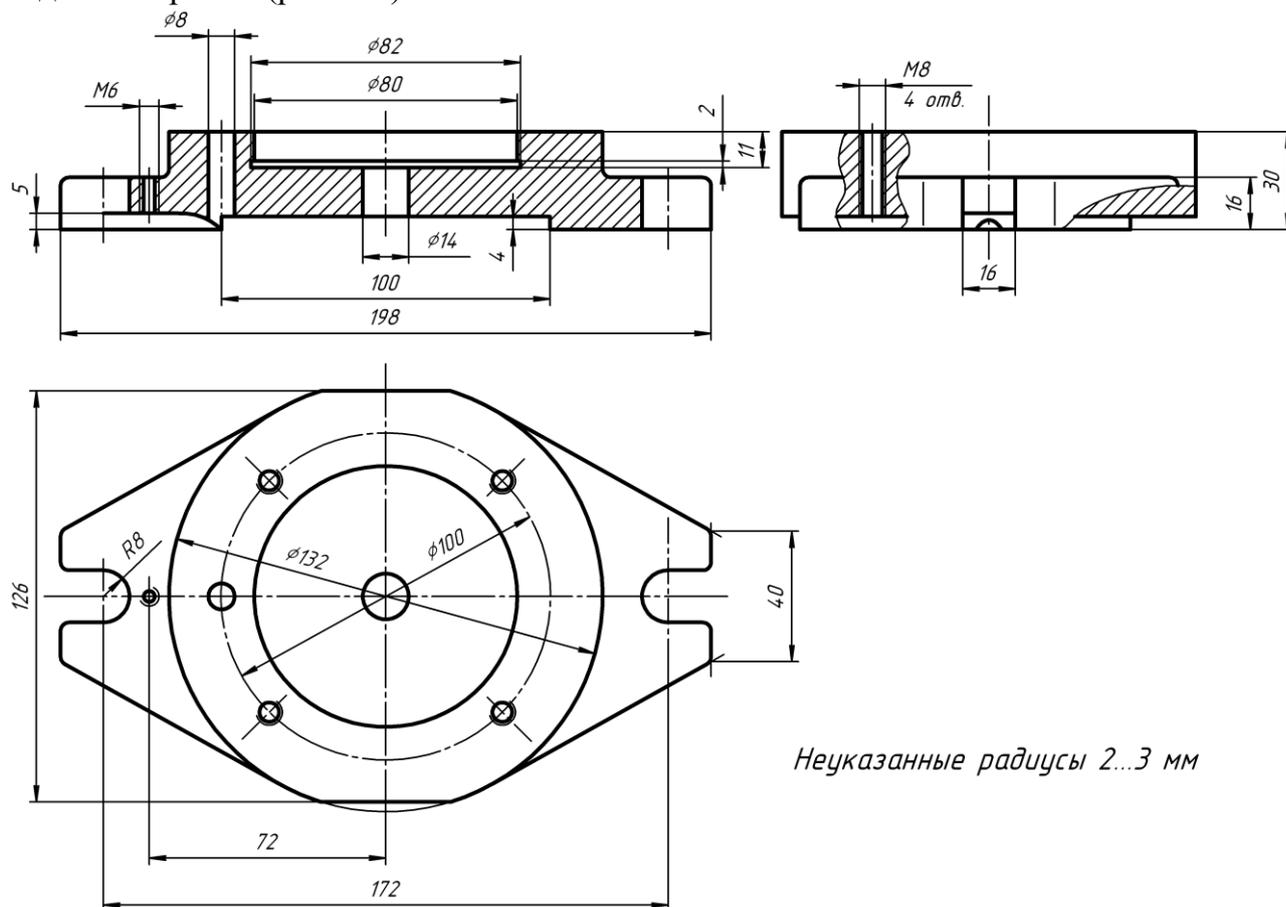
Расположение опорной плоскости литой детали параллельно основной надписи чертежа
